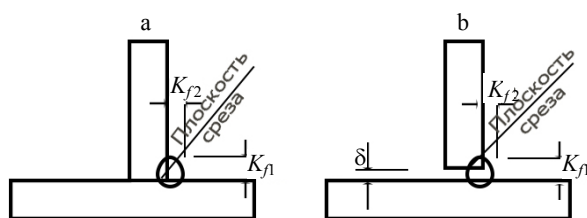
Сечения сварных швов в образцах, испытанных на сдвиг, без зазора (а) и с зазором (б)
